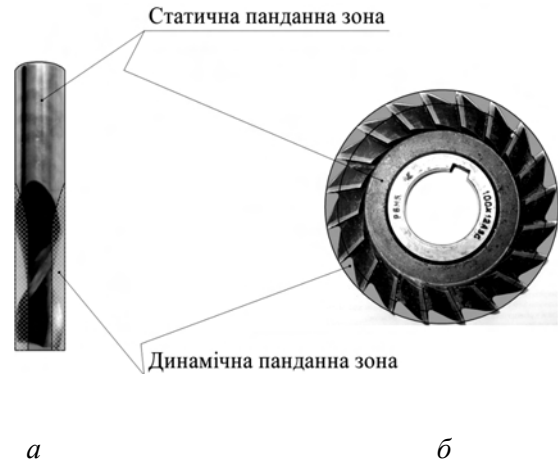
Загальний вигляд первинних панданних зон фрезерного інструмента: а - пальцевої фрези; б - дискової фрези
